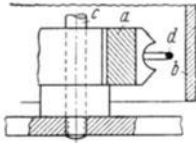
Aufhängevorrichtung und Abschirmung für einen Formfräser. a = Werkzeug; b = Anode; c = Dorn mit Haltescheibe und Abstandsstück; d = Abchirmdraht für die Kanten.
